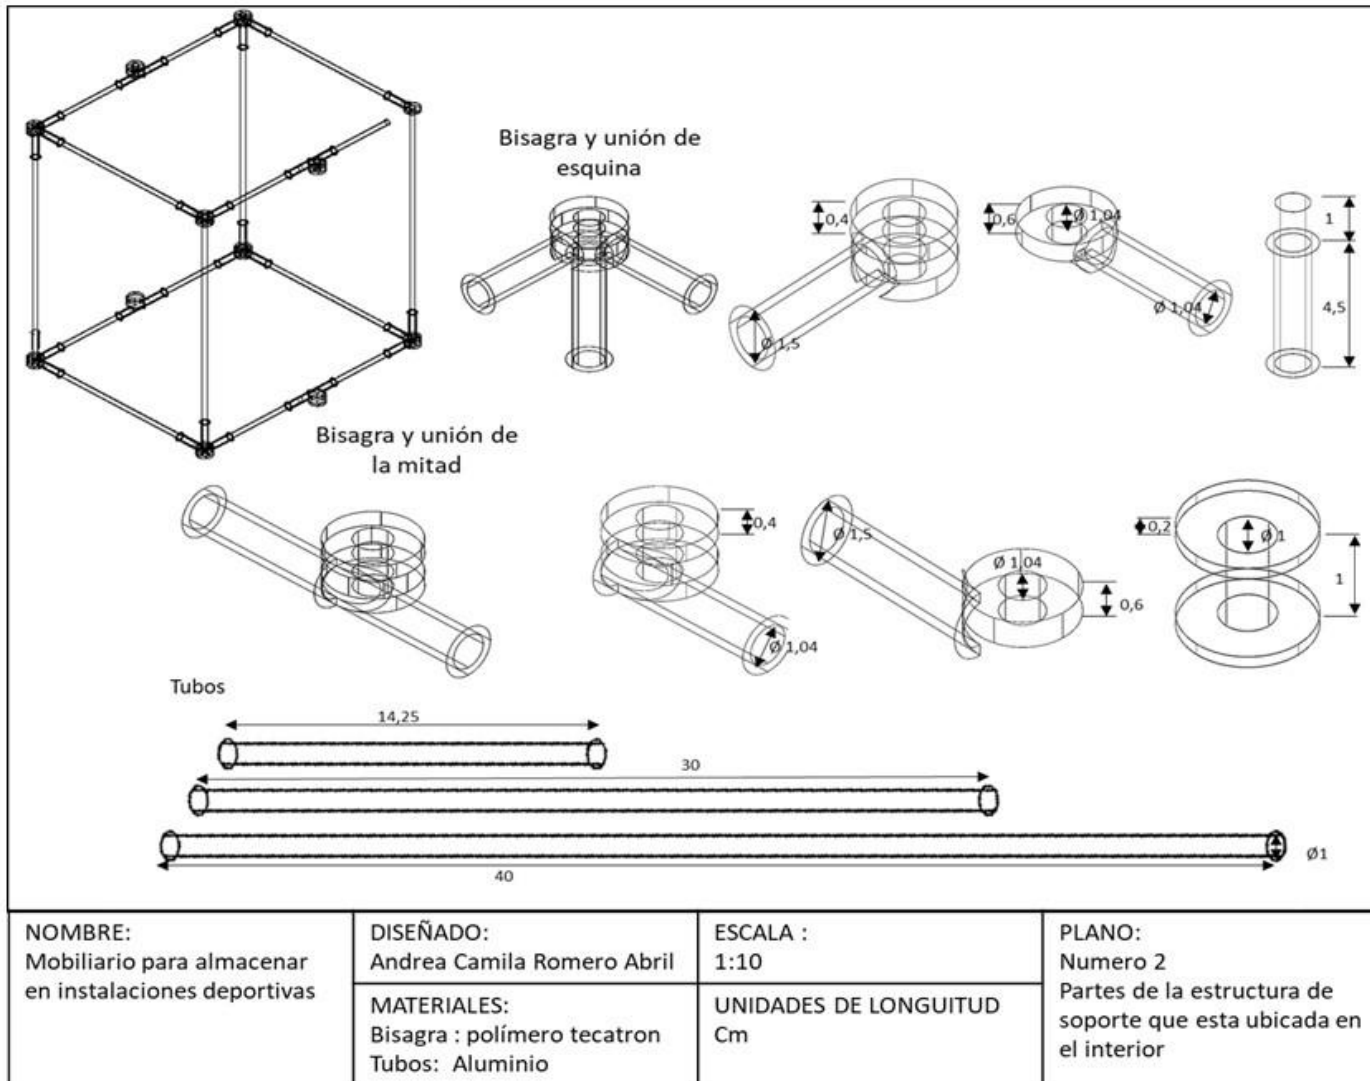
Plano de la parte de la estructura de soporte. Fuente: Elaboración propia
